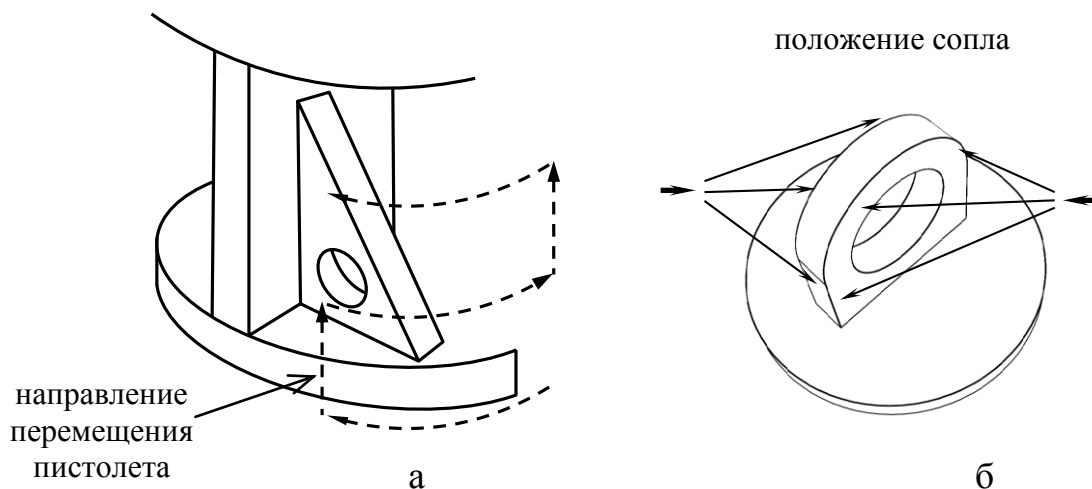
Схема нанесения покрытия на опору корпуса (а) и транспортировочную проушину (б)
